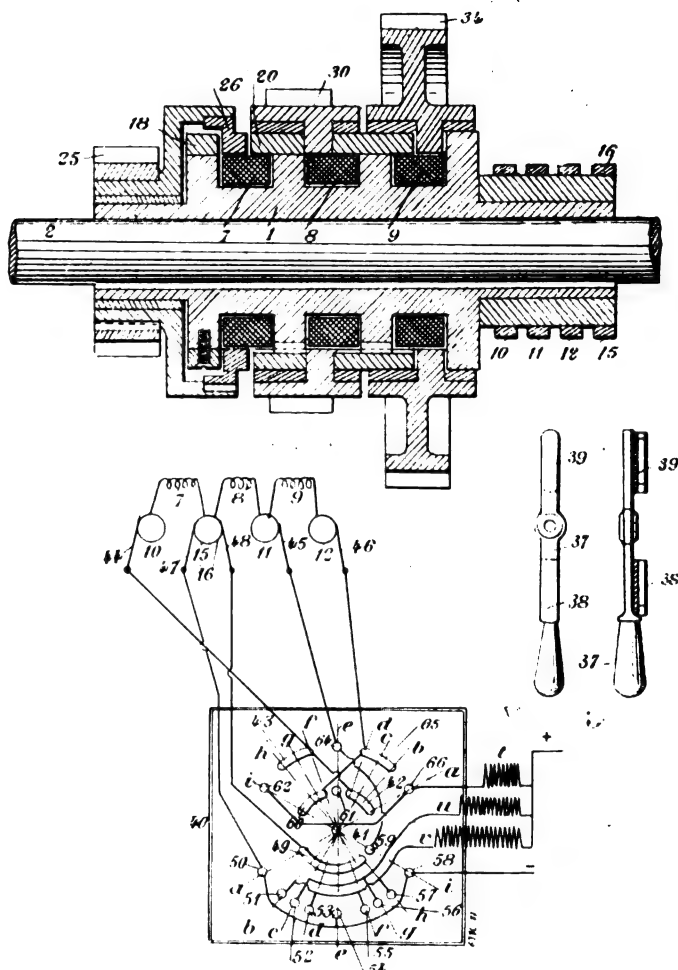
à 23. — Embrayage Crocker Wheeler.
